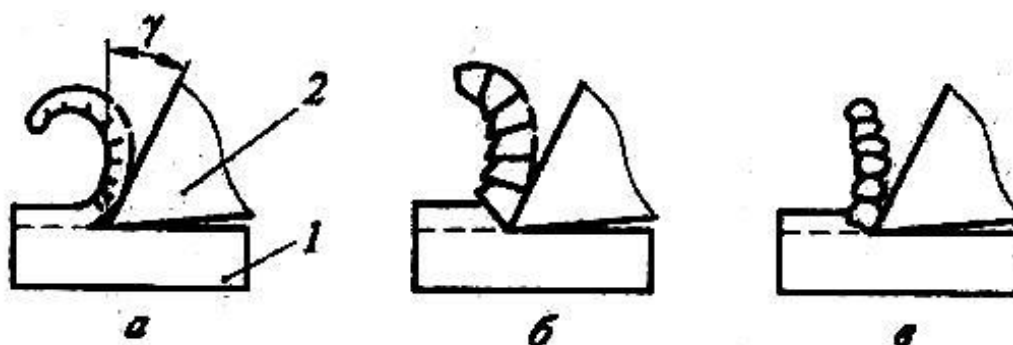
Види стружки: зливна (а); сколювання (б); надлому (в)
